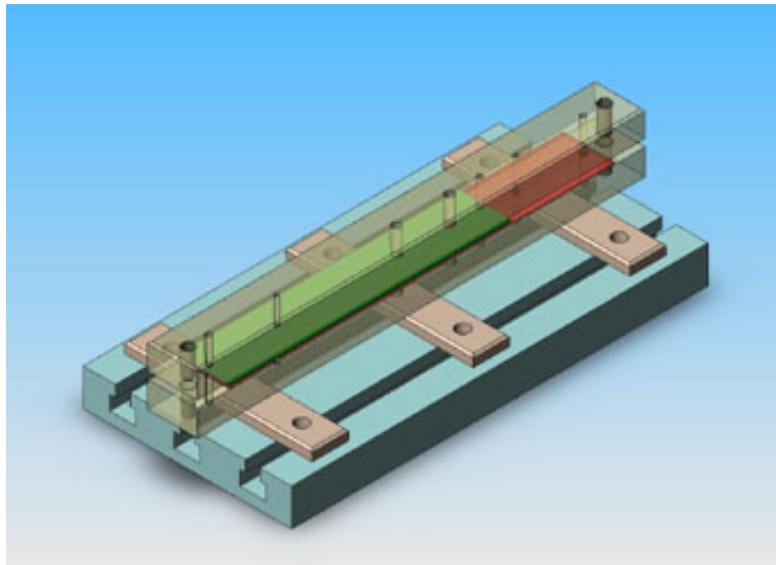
Dispositivo de fixação para o corte e furação de um provete
